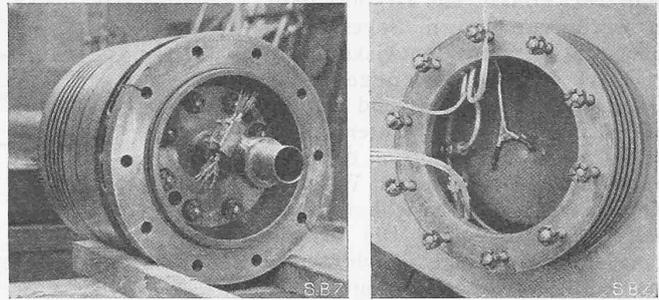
Einbau der Thermodrähte im Dieselmotor-Kolben.
